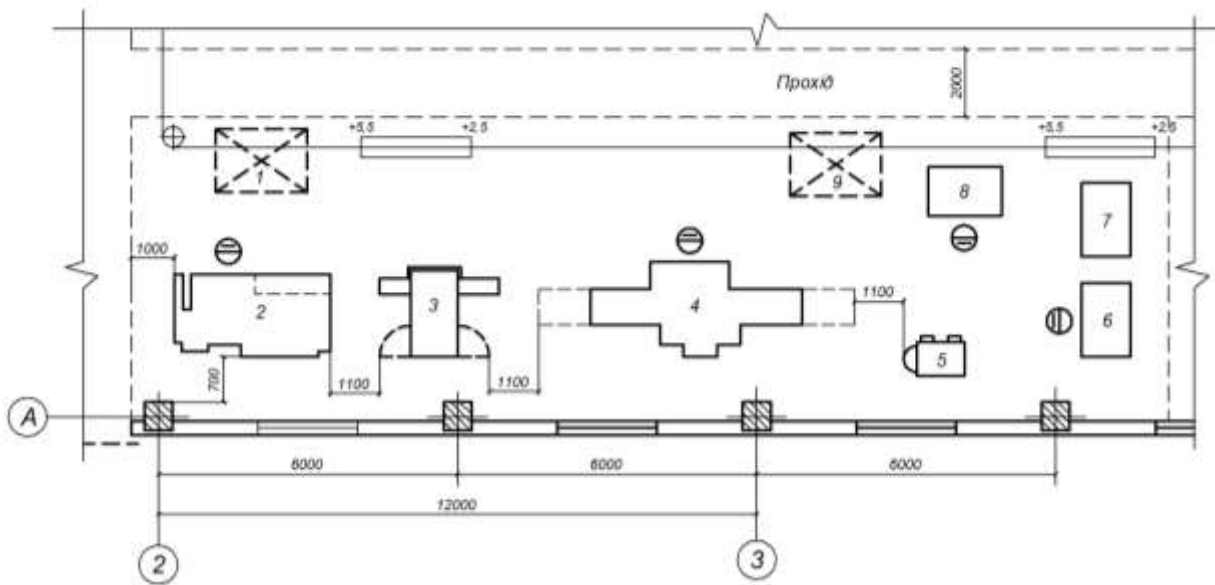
План розміщення обладнання на ділянці механічної обробки деталі «Півмуфта зубчаста КС6в – 07.602»: 1 – місце складування заготовок; 2 – токарний багаторізцевий півавтомат мод.1А720; 3 – вертикально-фрезерний мод.6Н10 ; 4 – горизонтально-фрезерний мод. 7Б56; 5 – вертикально свердлильний мод.2С132; 6 – слюсарний верстак; 7 – стіл для контролю ПР1460; 8 – промивочна машина М2А; 9 – місце складування деталей
